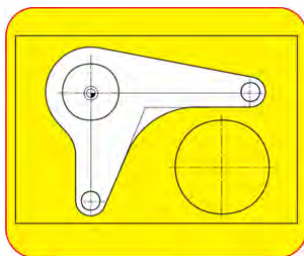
Schrumpfen und Schichten um den Hebel herum
